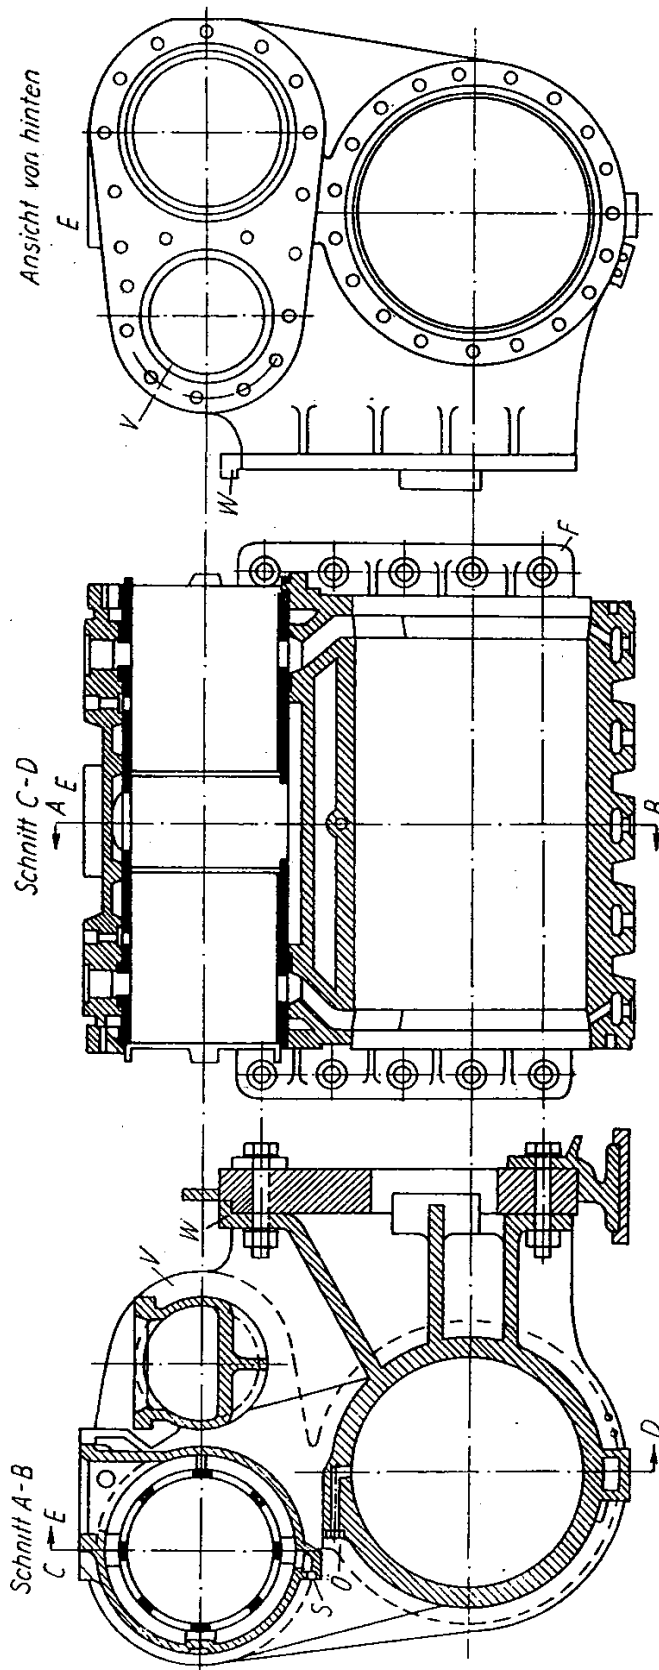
Zylinderblock einer Einheitslokomotive mit Druckausgleich-Kolbenschiebern (siehe auch Bild 71)
